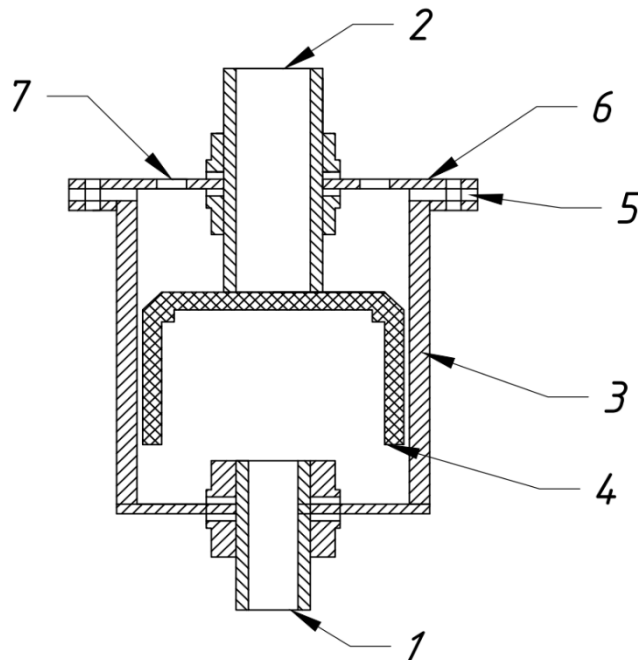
Датчик-прискорювач: 1 - штуцер випуску води із датчиком-прискорювача; 2 - штуцер гідравлічного зв'язка; 3 - корпус датчика - прискорювача; 4 - поплавок; 5 - ущільнення; 6 - кришка датчика; 7 - випускні отвори;
